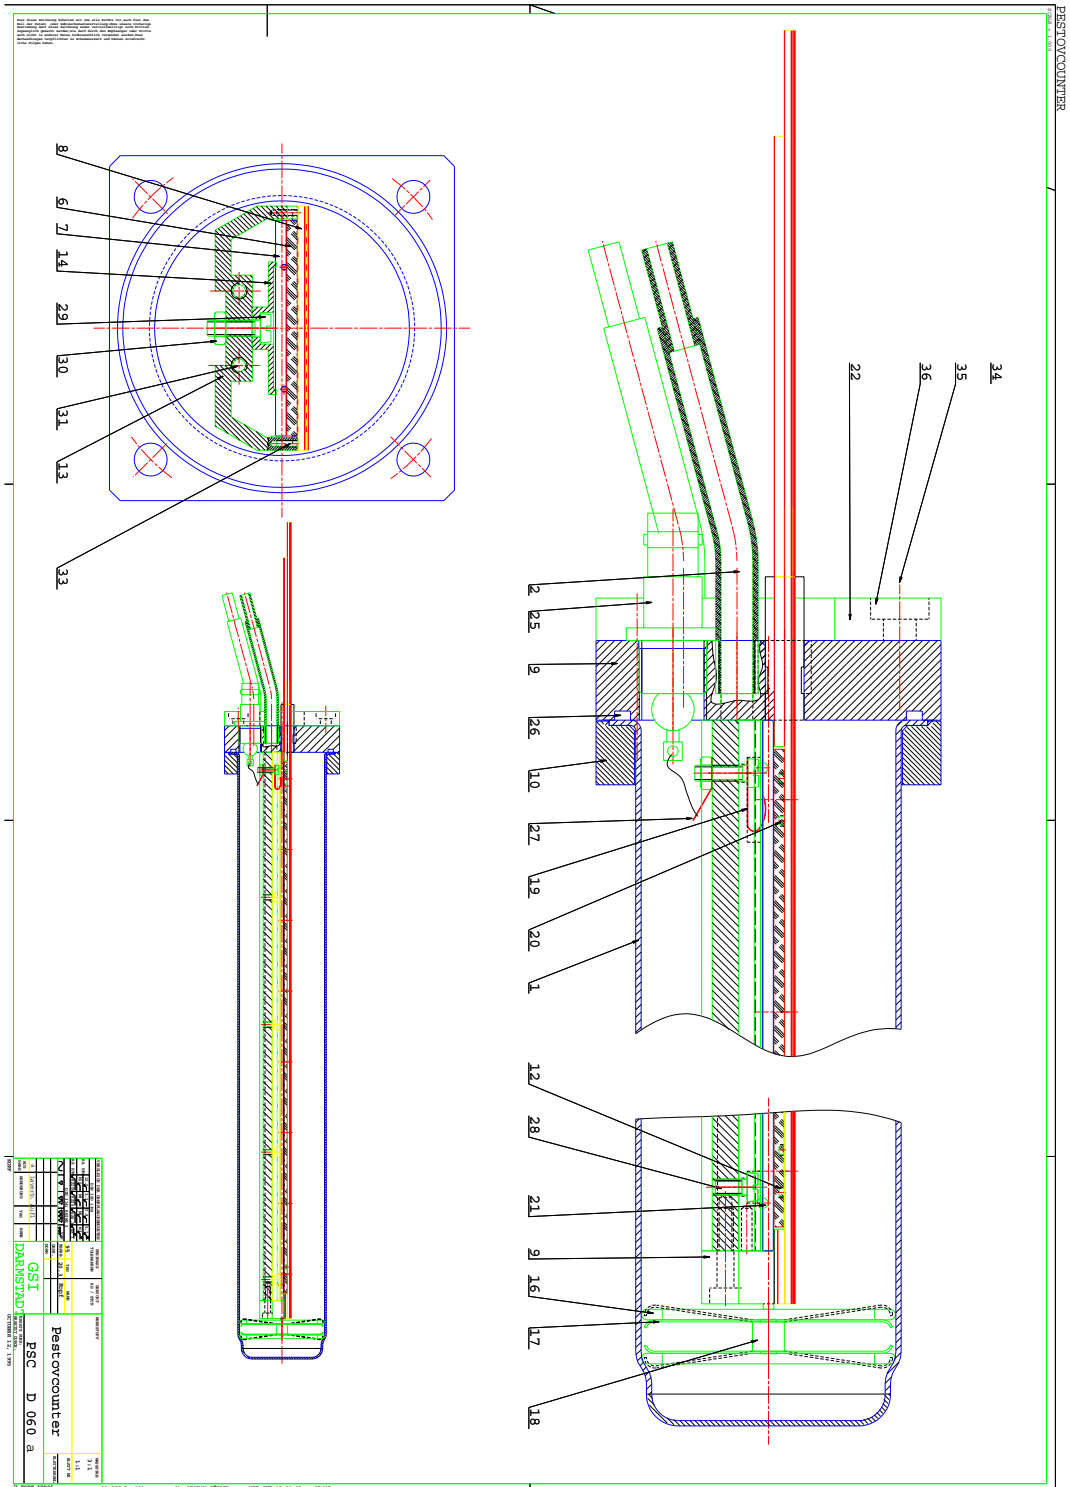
Die technische Zeichnung der Pestov-Zähler
